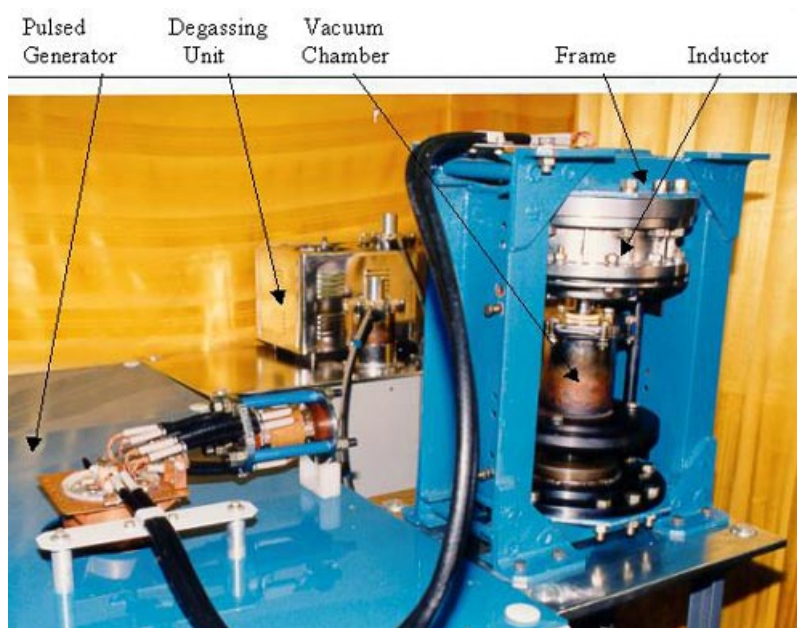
Внешний вид установки для магнитно-импульсного прессования
